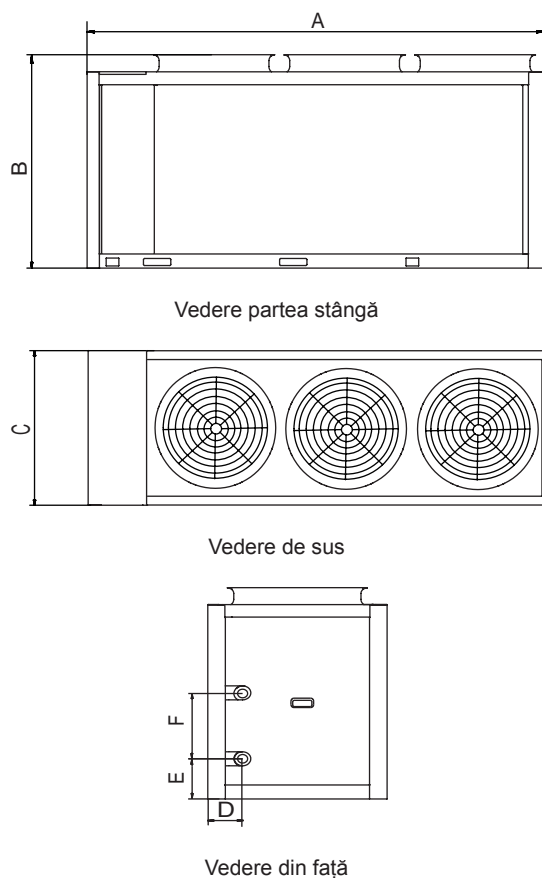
Schiță dimensională KEM-90 DNS3
